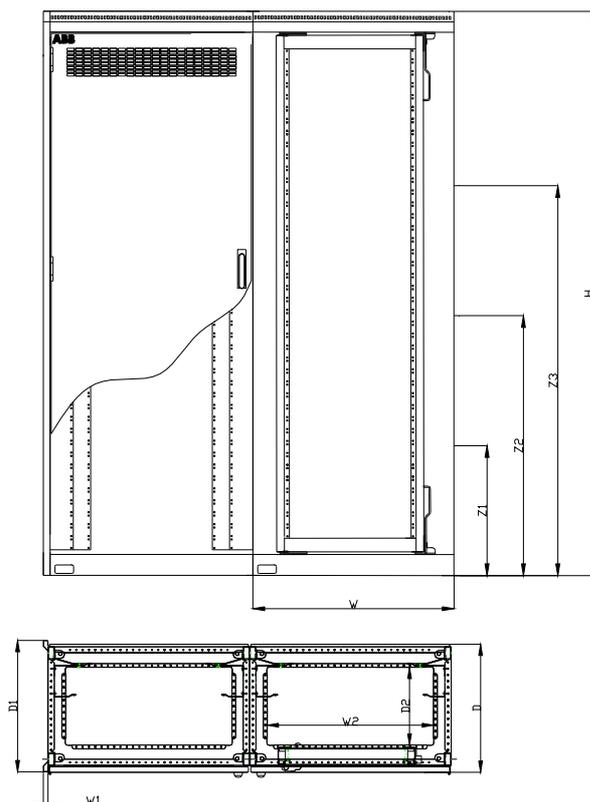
Verbinden der Schränke – Schraubenposition
